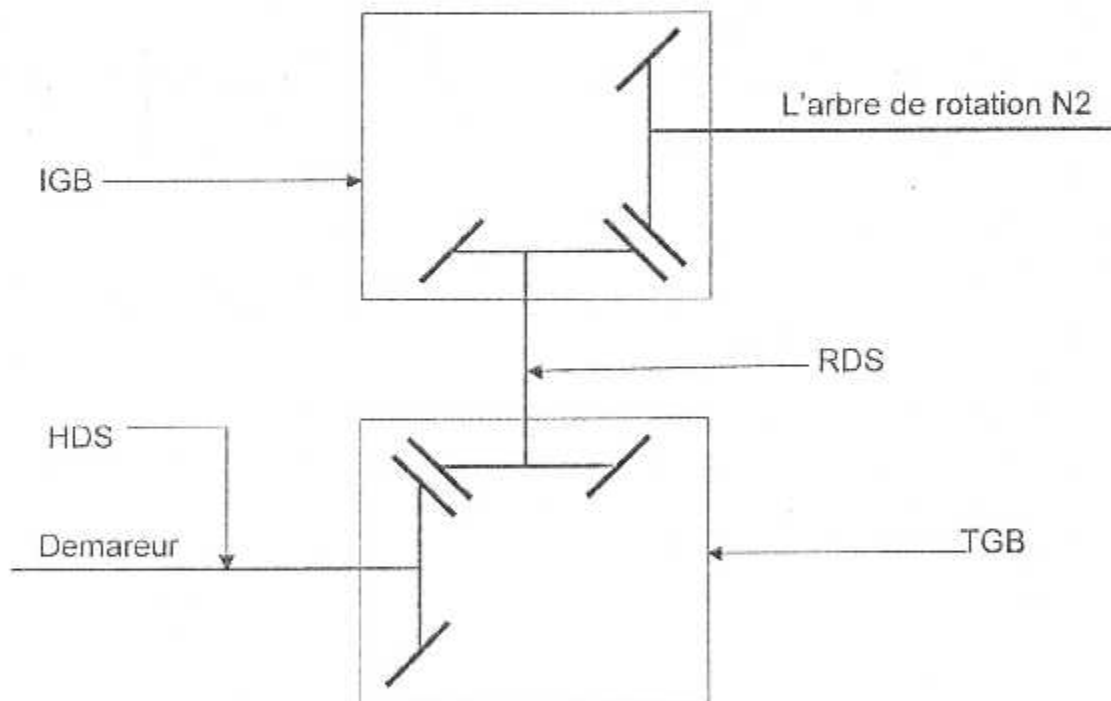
LES COMPOSANTES DE LA GEARBOX
